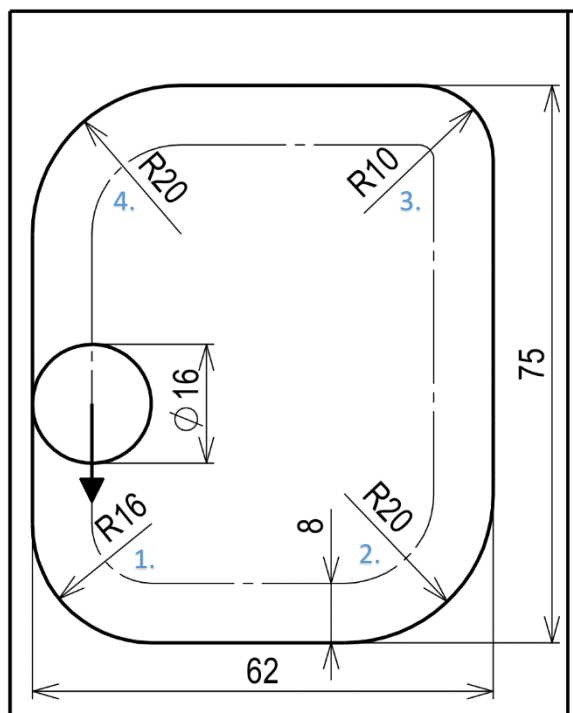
Nástroj pro obrábění kapsy experimentu [37]
